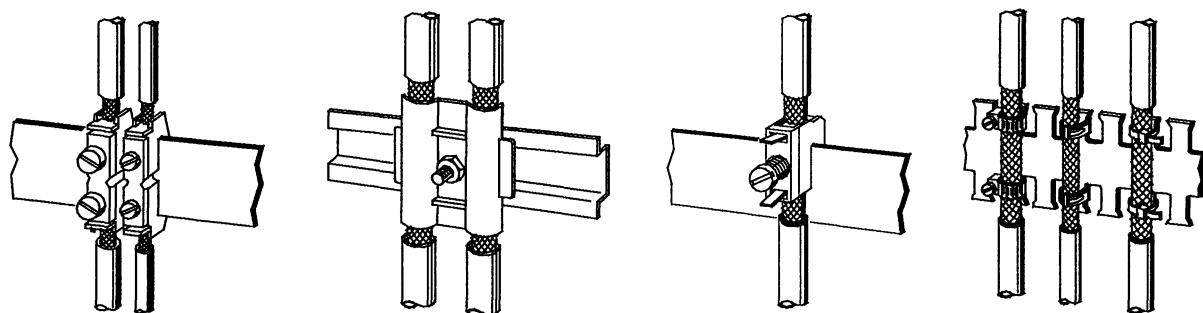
Fissaggio di cavi schermati con fascette fissacavo e fascette stringicavo
